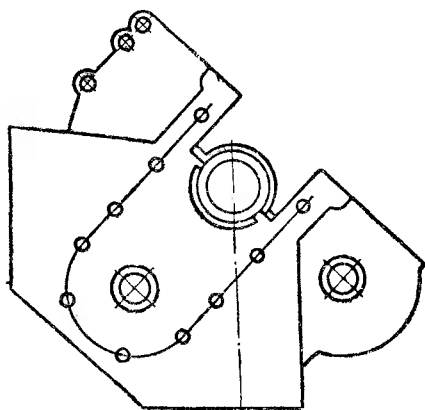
Положение блока цилиндров на конвейере при установке шатунов в сборе с поршнями
